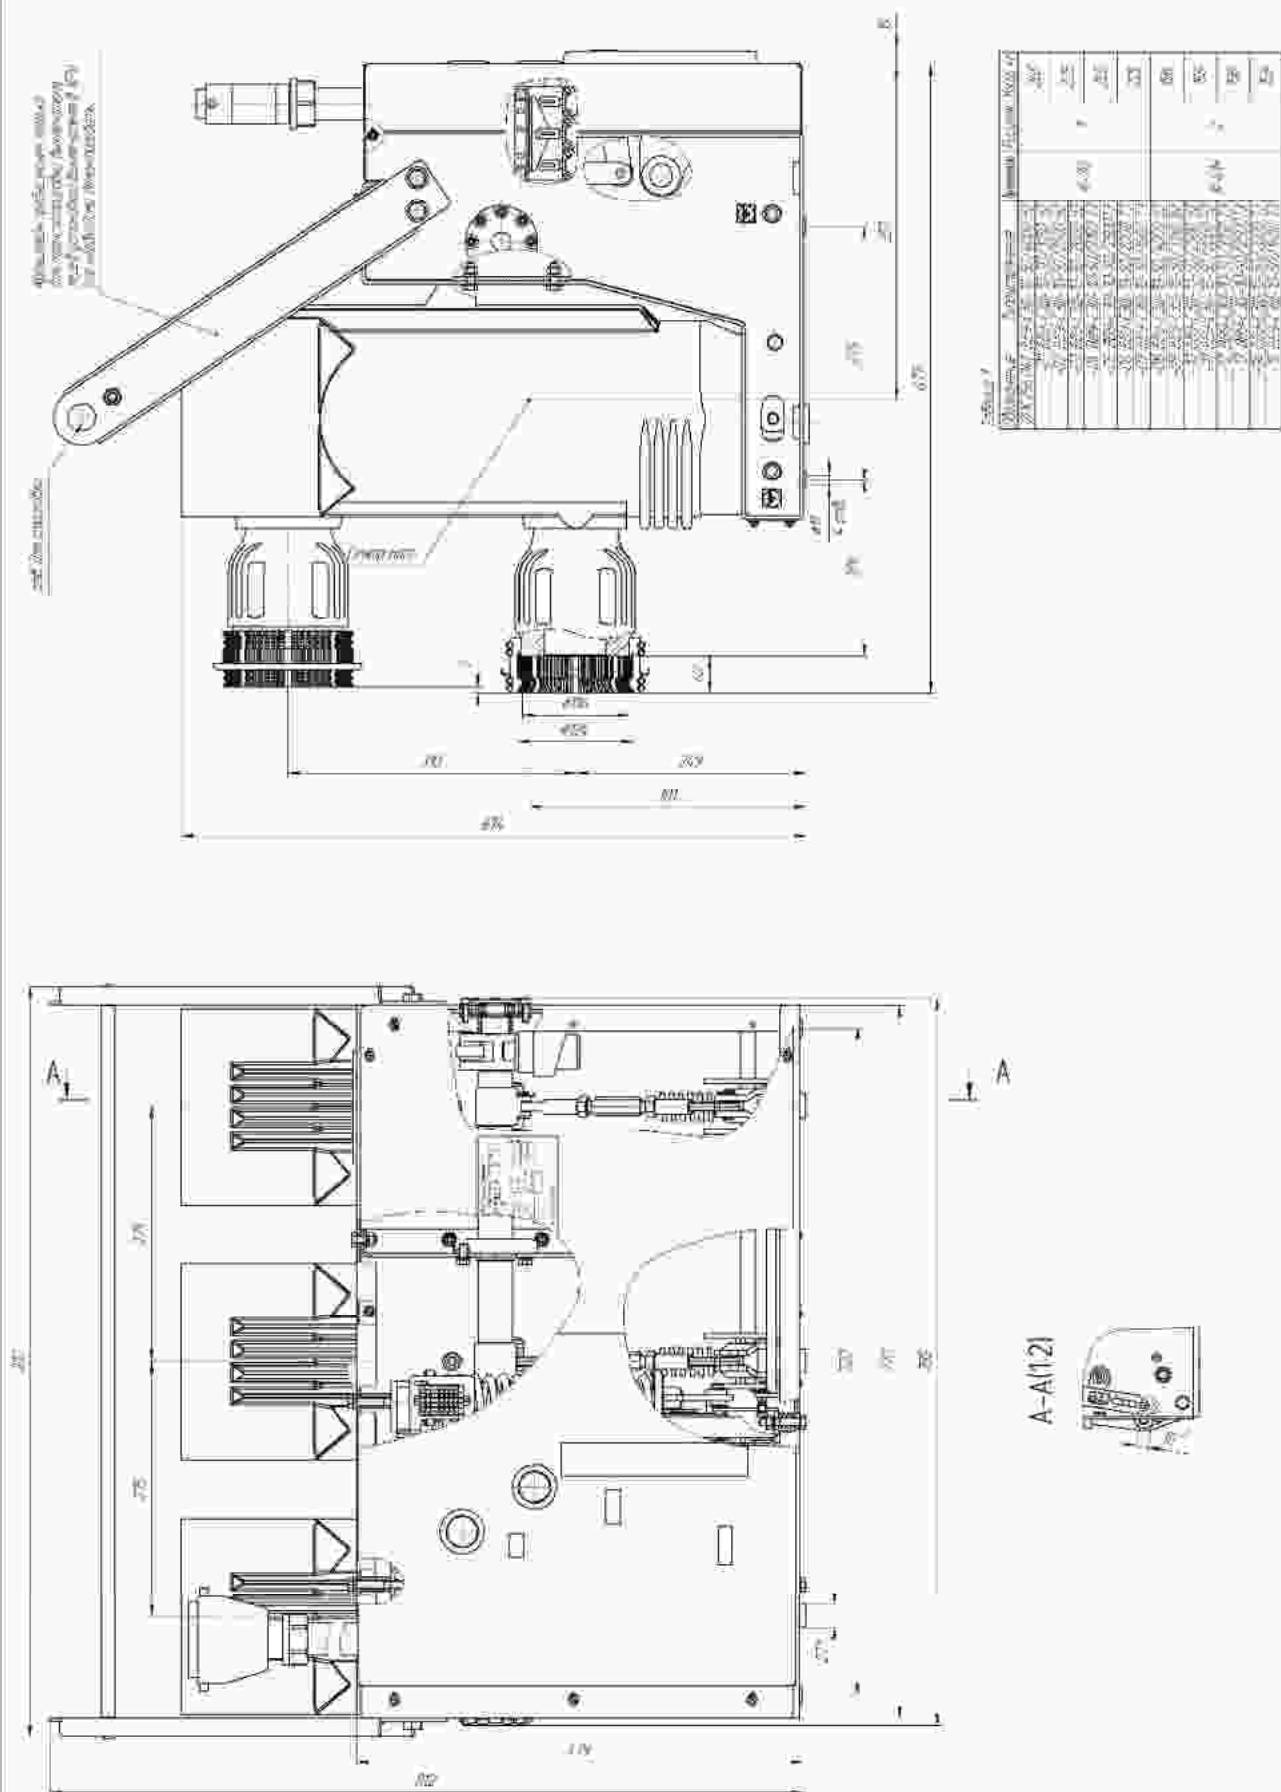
Газовитные, присоединительные и установочные размеры выключателя типа ВВУ-СЭЩ-П-(0-50)
